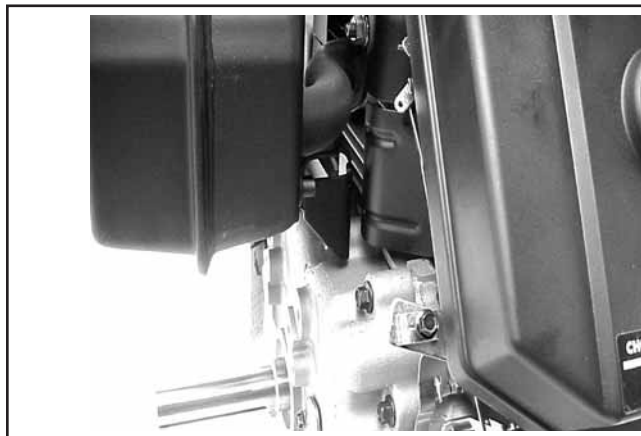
Réglage à distance d'accélérateur et de starter.
